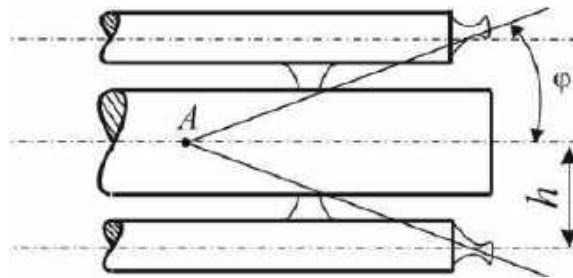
Прискорювач-пакет схеми "плюс"
